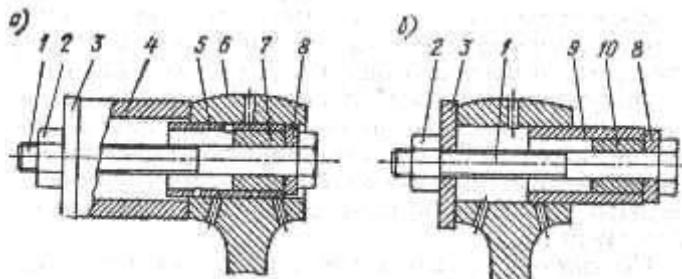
Приспособление для выпрессовки и запрессовки втулки верхней головки шатуна:
